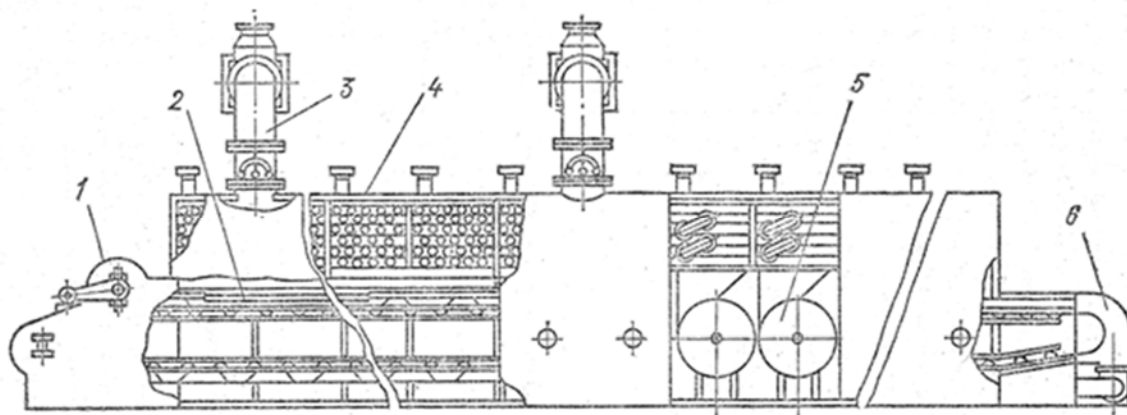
Схема стрічкової сушарки: 1 – завантажувальний шнек; 2 – стрічка; 3 – витяжка; 4 – калорифер; 5 – вентилятор; 6 – шнек розвантажувальний
